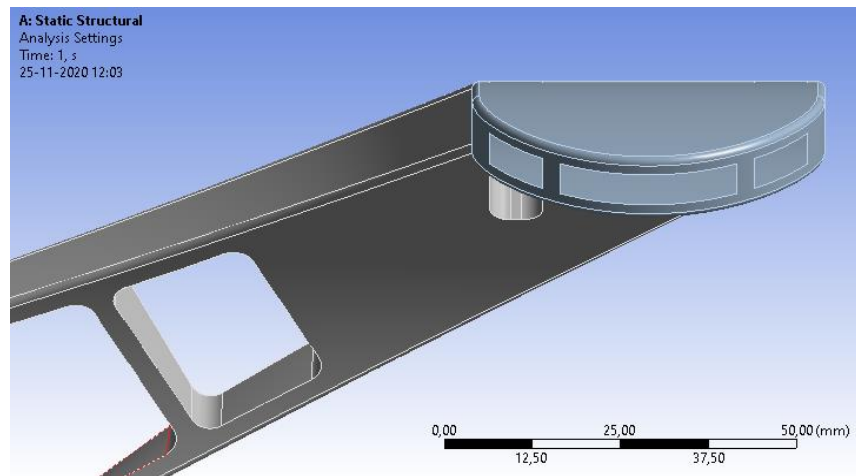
Vista 3 rediseño N°4 de eslabón pierna izquierda.
